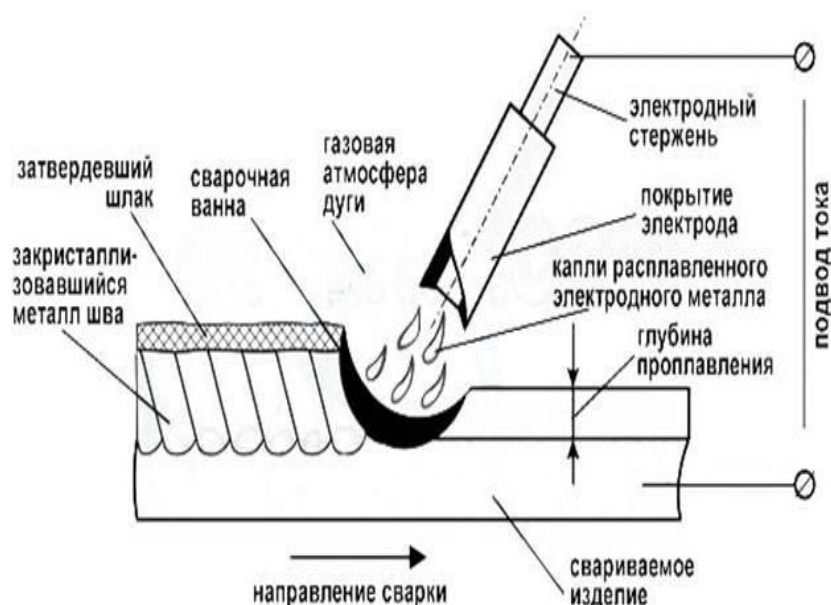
Эскиз ручной дуговой сварки покрытым электродом
